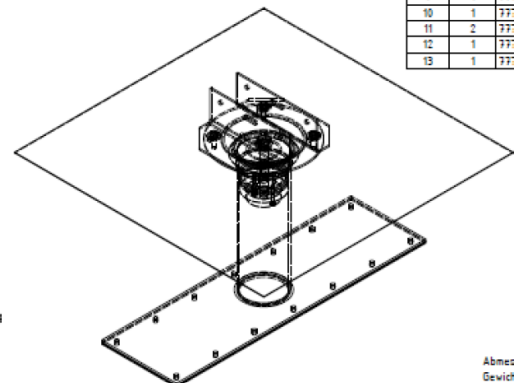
V2: Punkthalter für Dachpaneele, Beton
